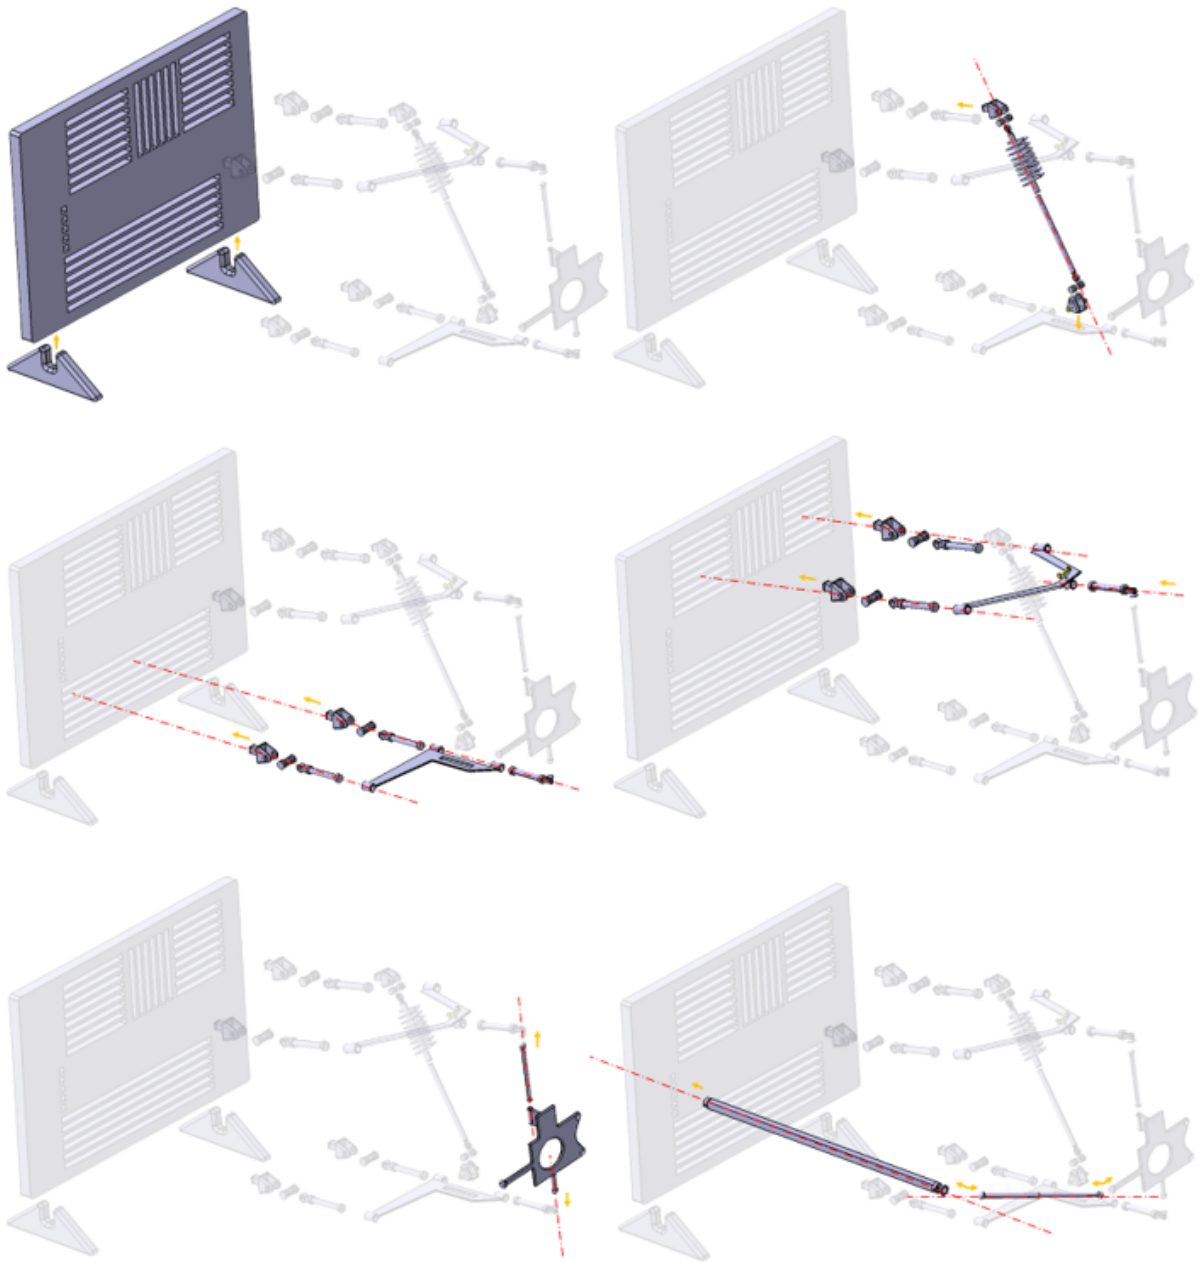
Explosión del ensamblaje de componentes del Gemelo Digital - versión Doble Trapecio.
